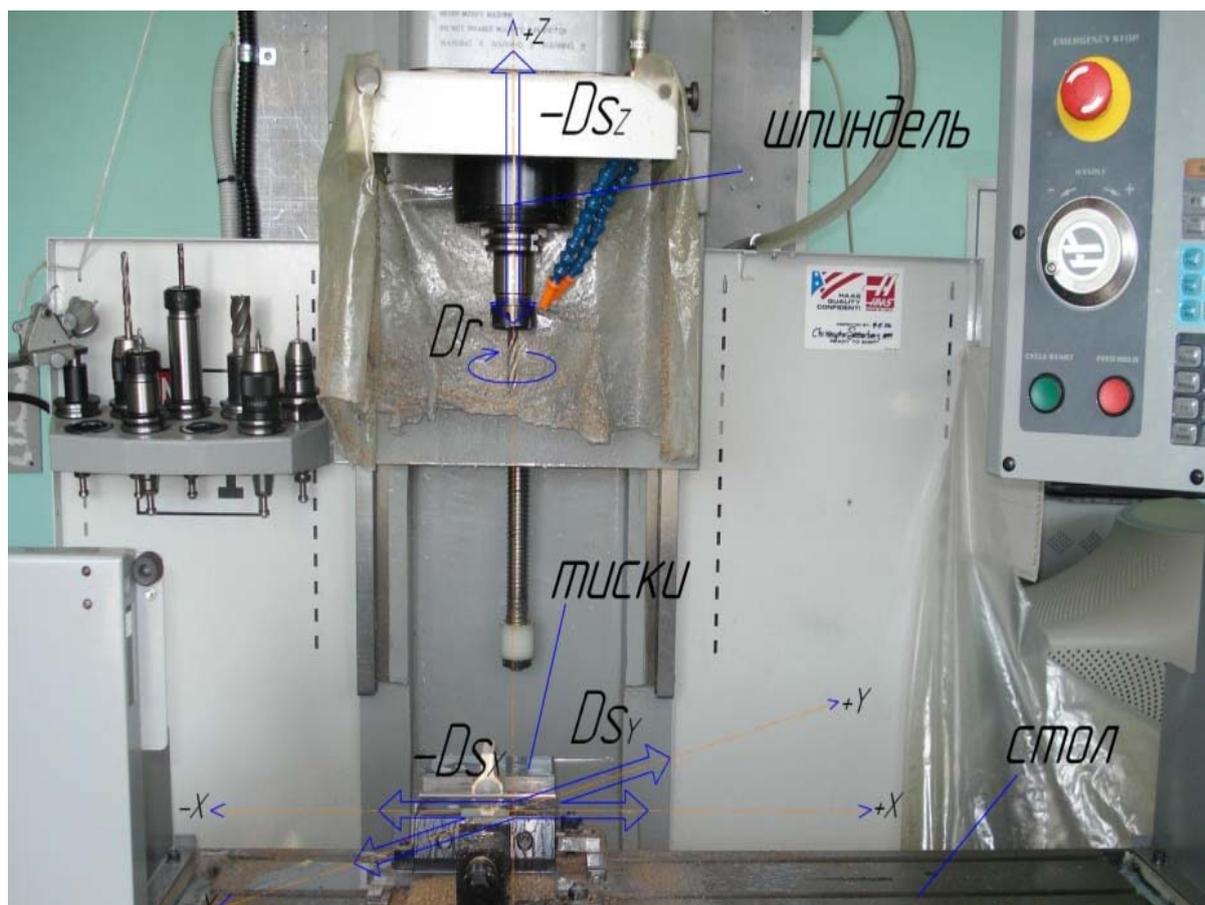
Рабочие движения исполнительных органов фрезерного станка с ЧПУ «НААС»
